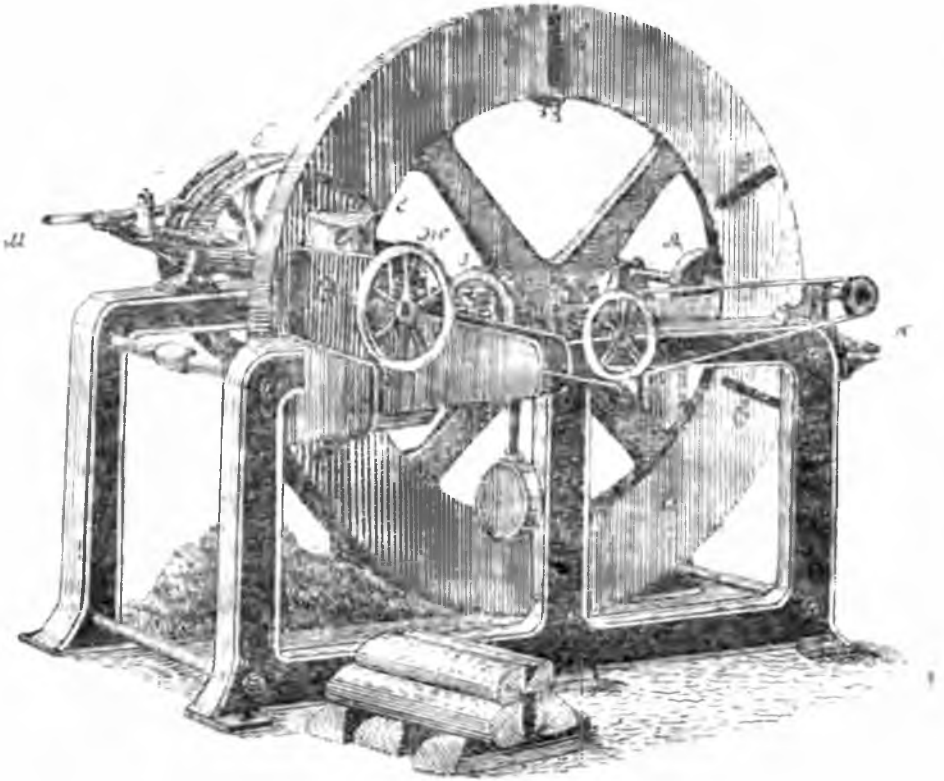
й. Ротативная машина фирмы Шранц и Роллгер: *а*—шайба, насаженная на рабочем валу; *б*—два шкива, на том же валу; *в*—габаритная резцов, укрепленная в шайбе; *г*—строгальный нож; *д*—коробка, в которую вкладываются отрубки; *е*—перерабатываемый отрубок дерева; *ж*—колесо, служащее для отодвигания металлической дощечки, прилегающей к отрубку; *з*—ролик с подвешенным к нему грузом, благодаря которому вышеупомянутая дощечка надавливает отрубок на шайбу; *и*—суппорт точильного аппарата; *к*—наждаковый круг для оттачивания орудий; *л*—рычаг для перевода ремня на шкивах.
